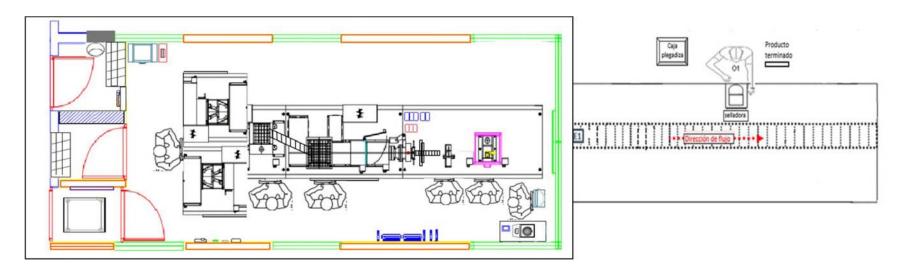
Vista en planta del área de manufactura de semisólidos luego de la propuesta.
